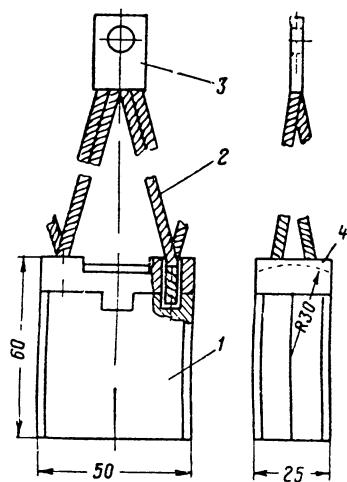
Разрезная щетка с резиновым амортизатором:
